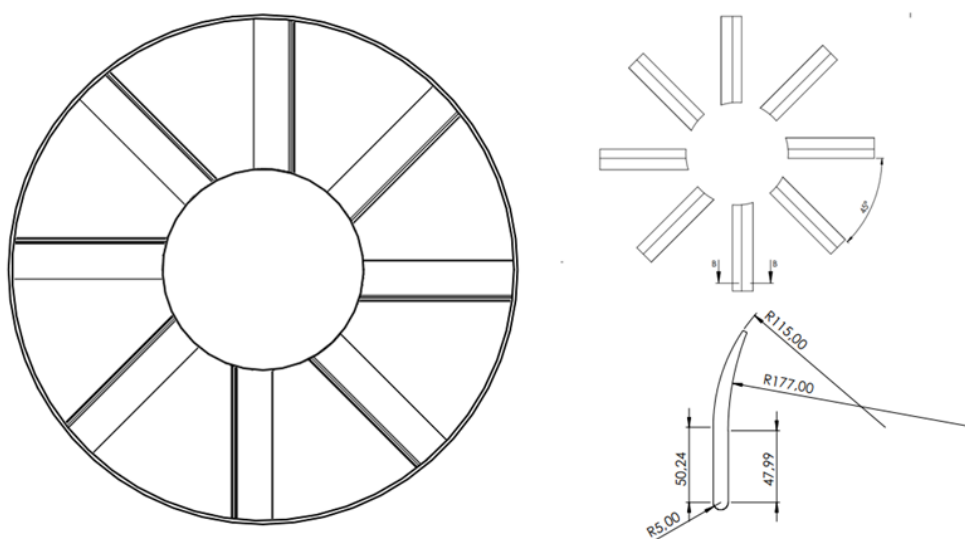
Vista frontal de montagem das diretrizes e dimensões do perfil.
